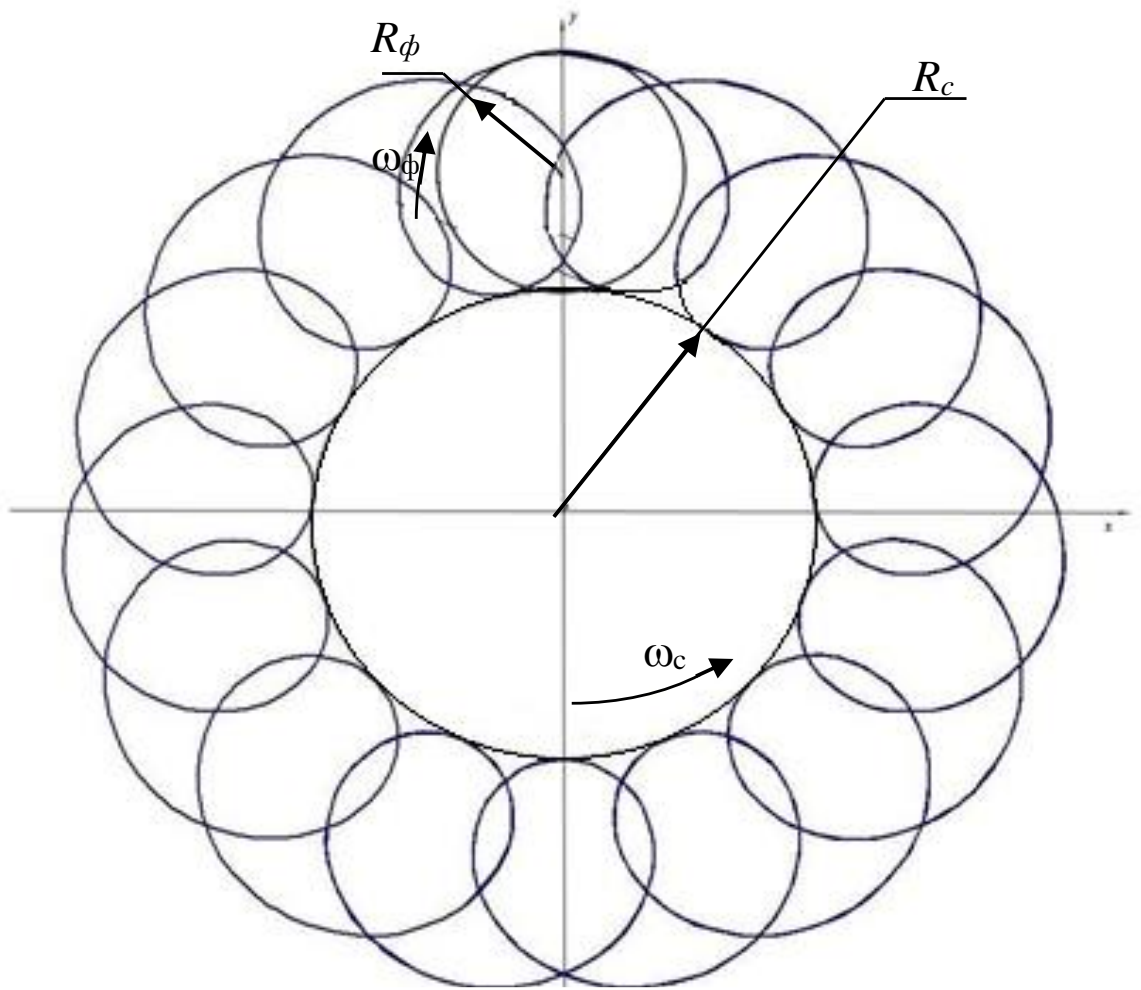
Траєкторія руху фрези при зустрічному фрезеруванні опуклого контуру
